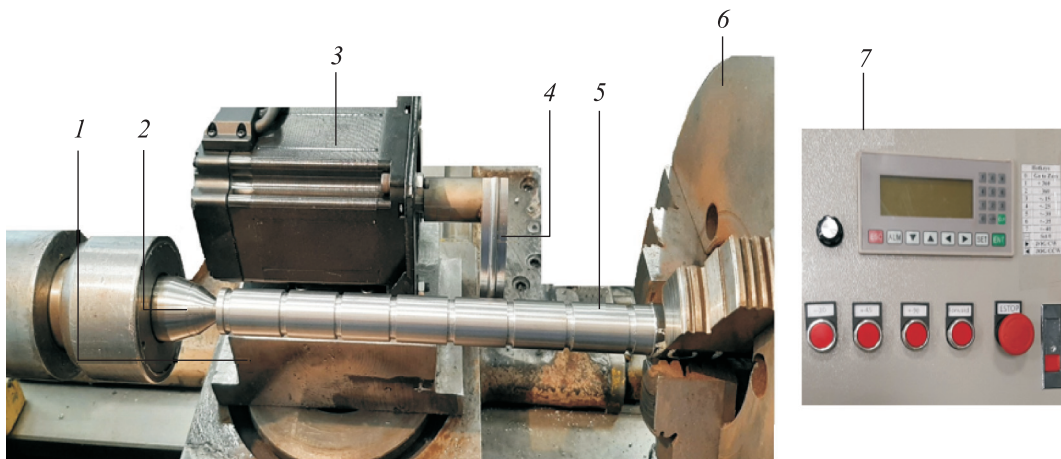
Внешний вид устройства для маятникового ППД наружных поверхностей цилиндрической детали:
